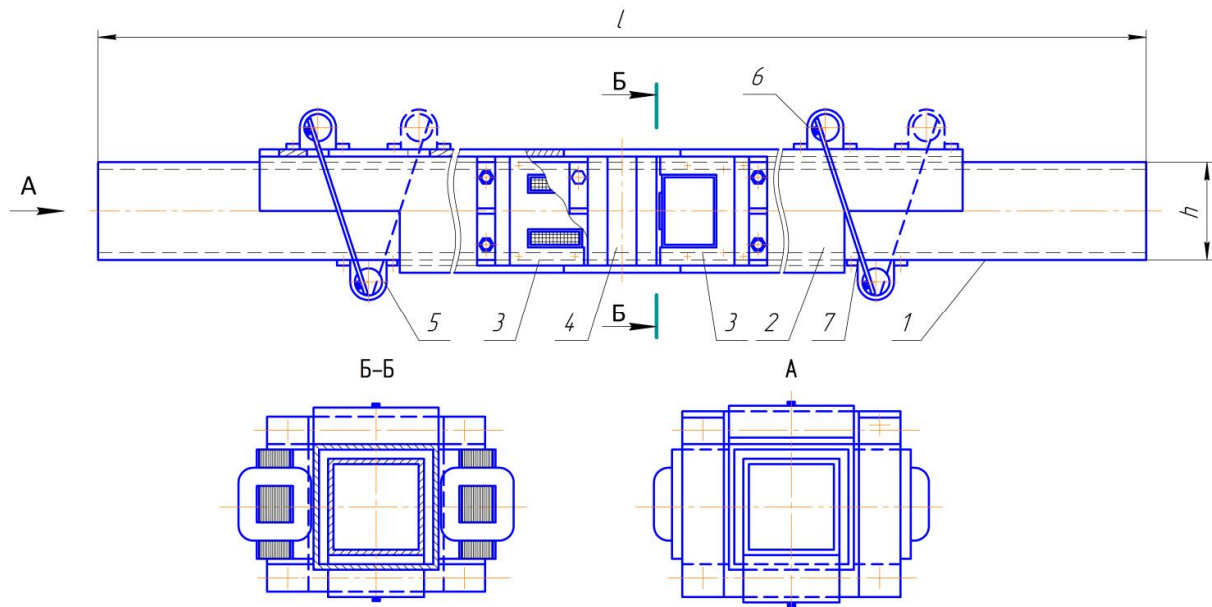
Конструктивна схема трубчастого конвеєра зі суміщеними центрами коливальних мас: 1 – транспортувальний орган; 2 – реактивна маса; 3 – статор та 4 – якорь електромагнітного приводу; 5 – плоскі пружини; 6 – нерухомий шарнірний кронштейн; 7 – рухомий шарнірний кронштейн
